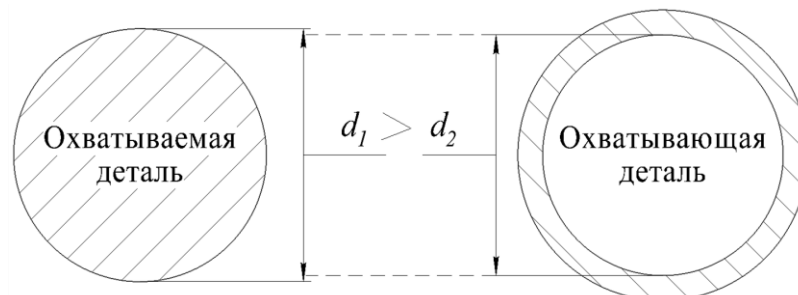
Размеры деталей прессового соединения: d_1 – диаметр охватываемой детали; d_2 – диаметр охватывающей детали
